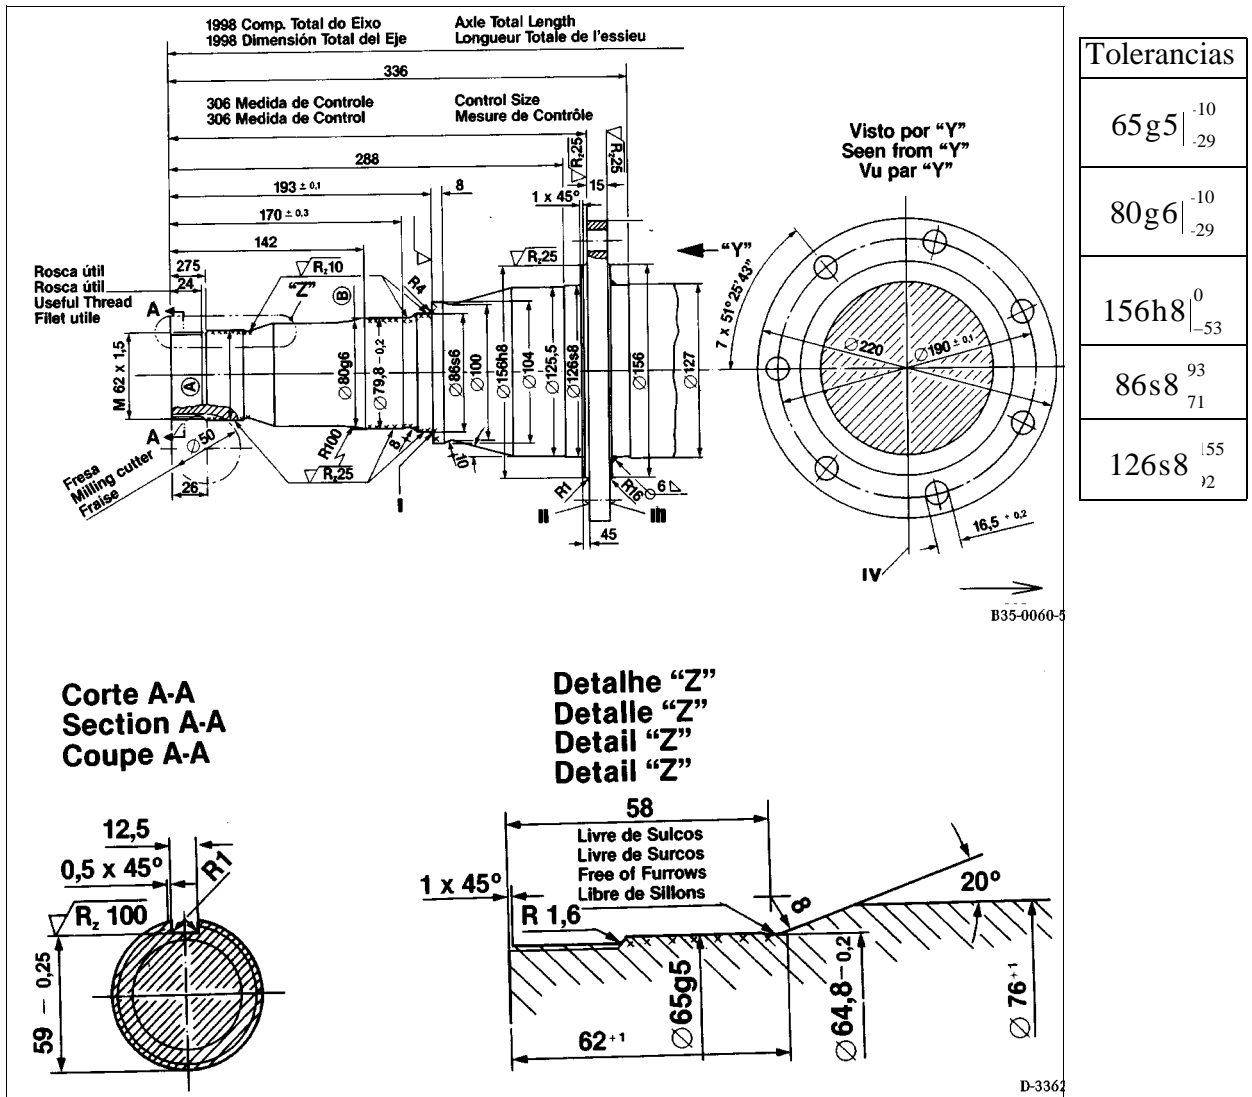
Maquinado de los extremos del eje (HL 4/25D - 7,6; HL 4/60D - 7,6)
